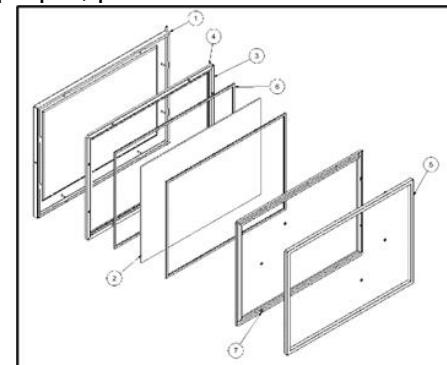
Vue éclatée de l'assemblage de la porte
